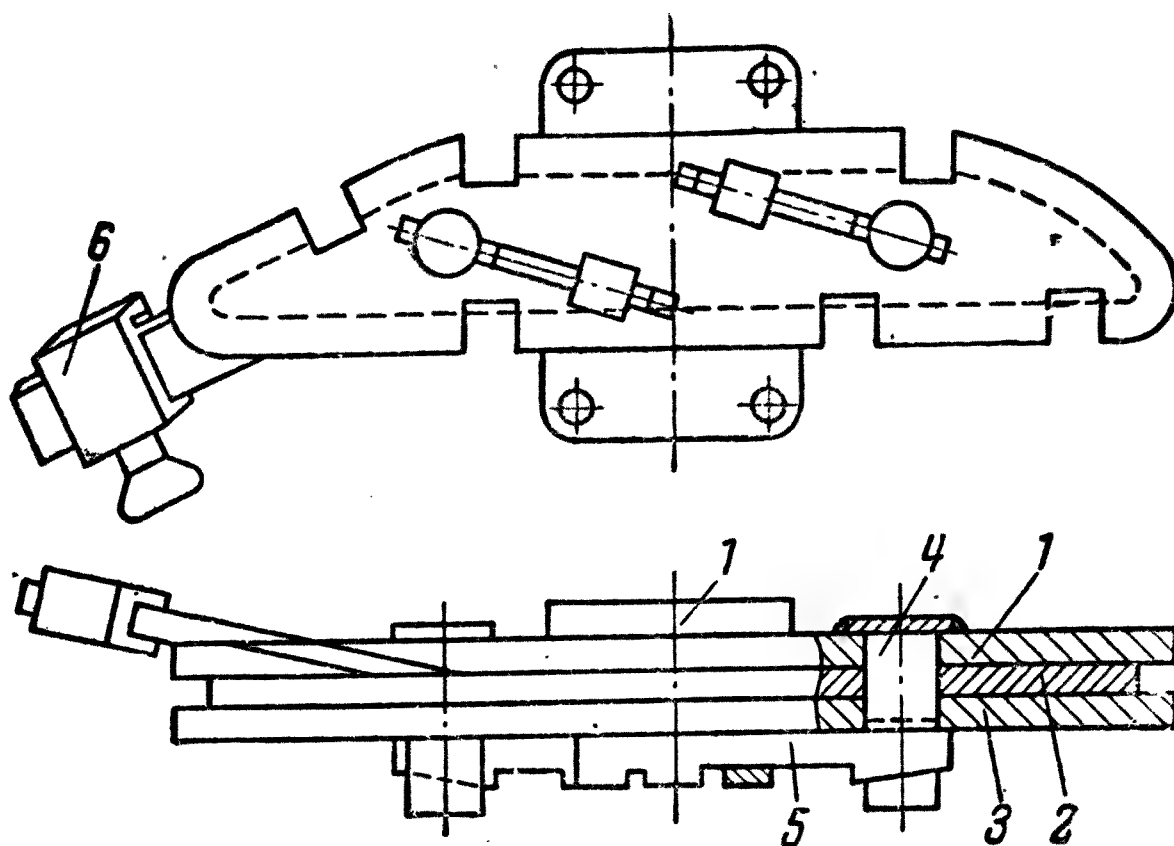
Шаблон-лодочка для намотки секций двухслойной обмотки
